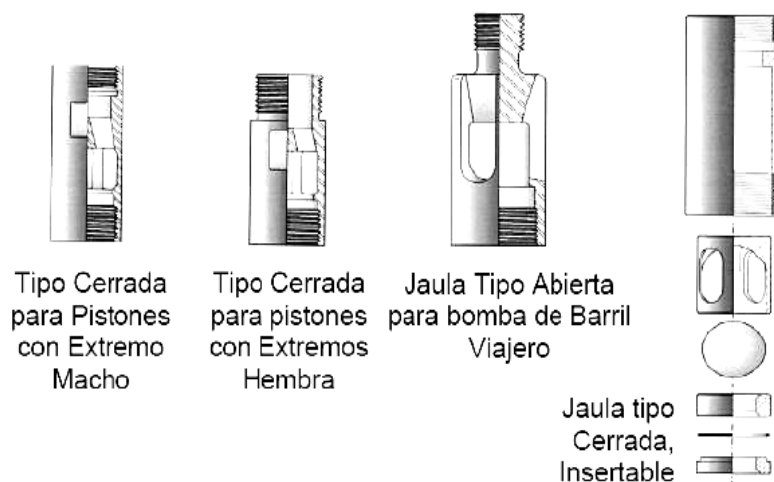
Tipos de Jaulas Válvula Viajera
